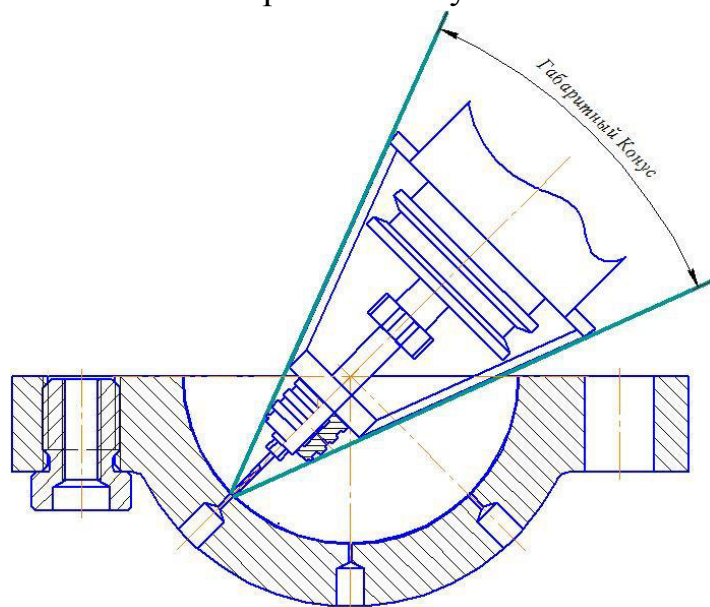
Схема обработки канавки радиусной формы фрезой с удлинительной оправкой и кондукторным приспособлением
